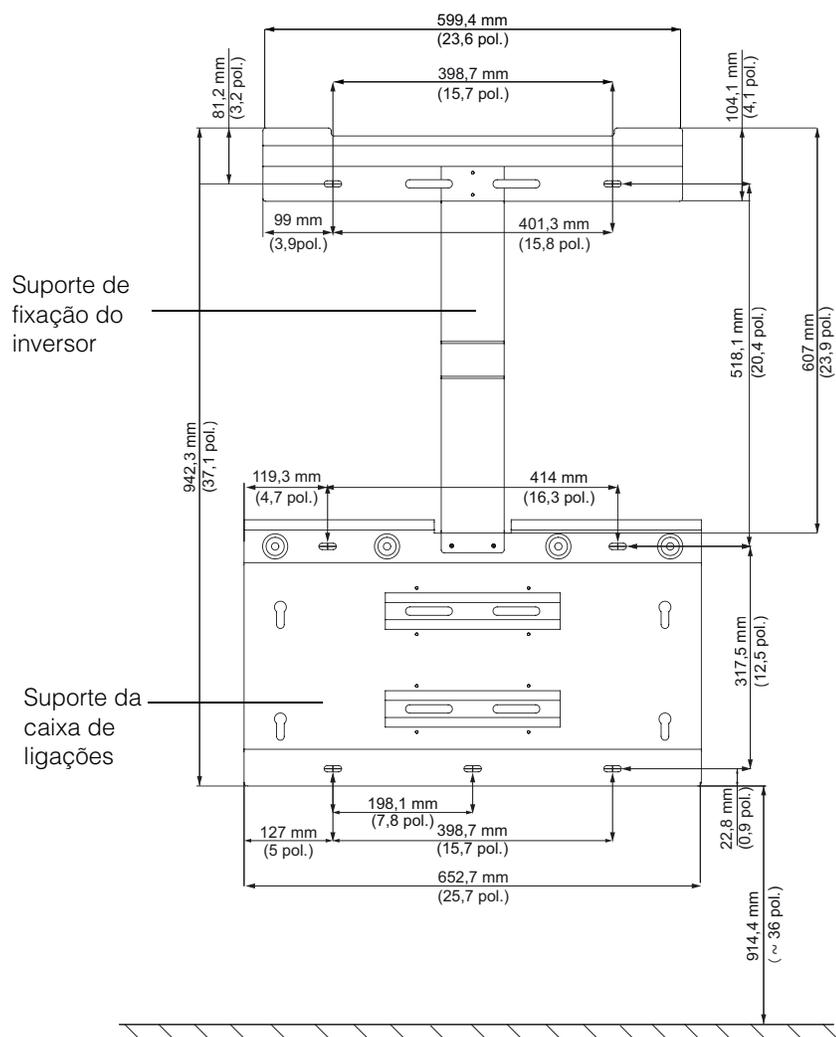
Dimensões dos suportes de fixação – Caixa de ligações e inversor
